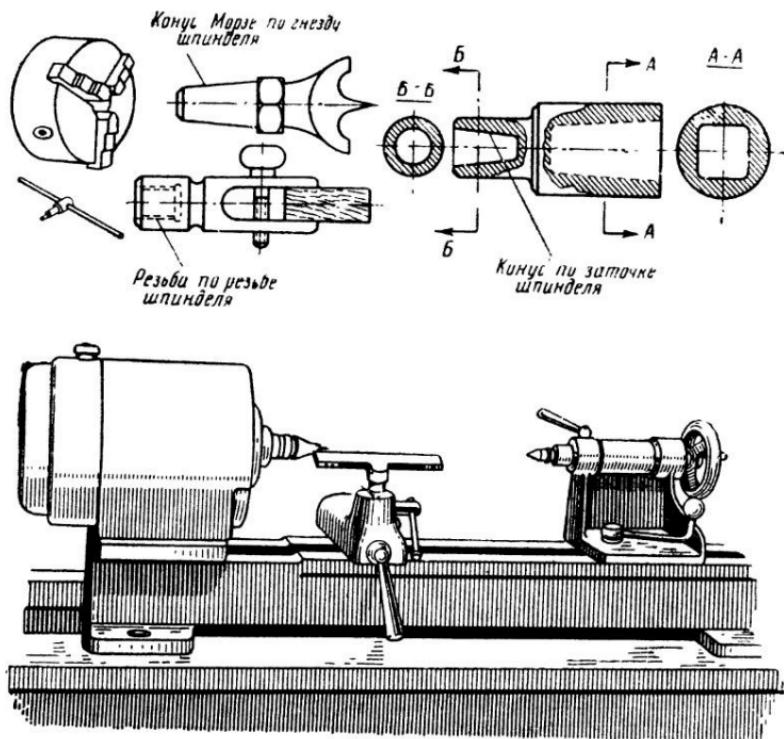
Самодельный токарный станок для обработки древесины и крепежные приспособления к нему.
